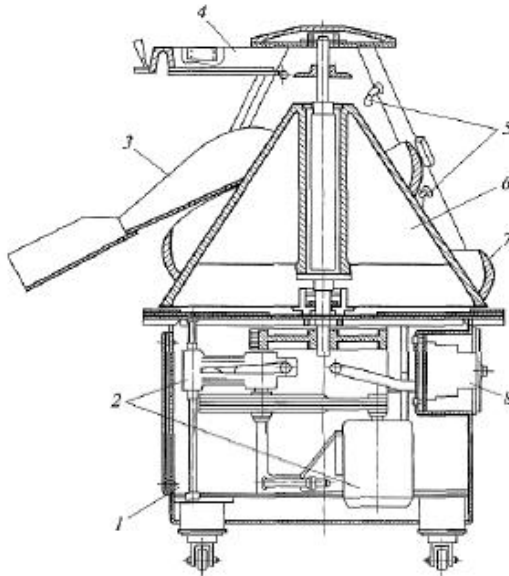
Машина для округлення тіста А2-ХПО/6: 1 – корпус; 2 – привод; 3 – лоток; 4 – борошнопідсипач; 5 – повітродувний пристрій; 6 – конус; 7 – спіраль; 8 – електричне обладнання
